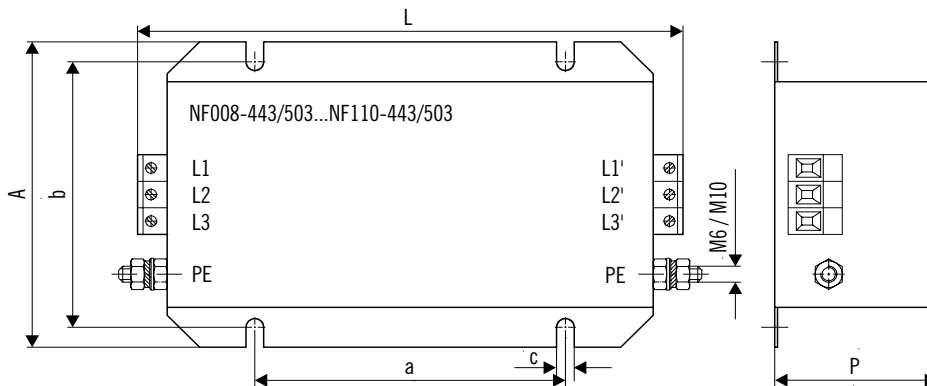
Desenho dimensional para filtros de entrada NF...-...
